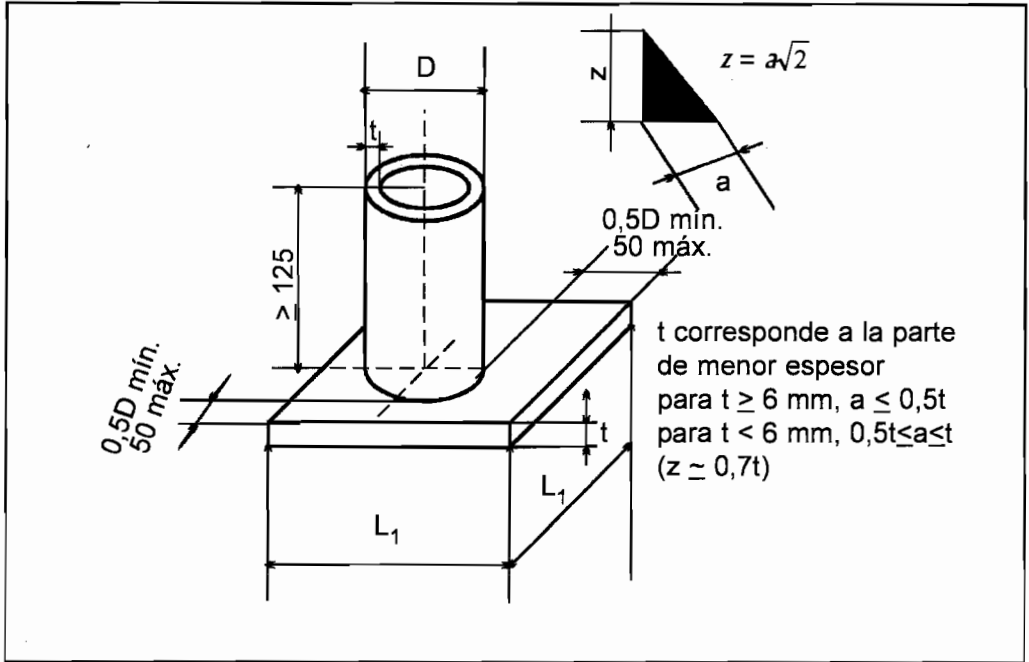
DIMENSIONES DEL CUPÓN DE PRUEBA PARA EL SOLDEO DE TUBOS EN ÁNGULO (DIMENSIONES EN MILÍMETROS)
